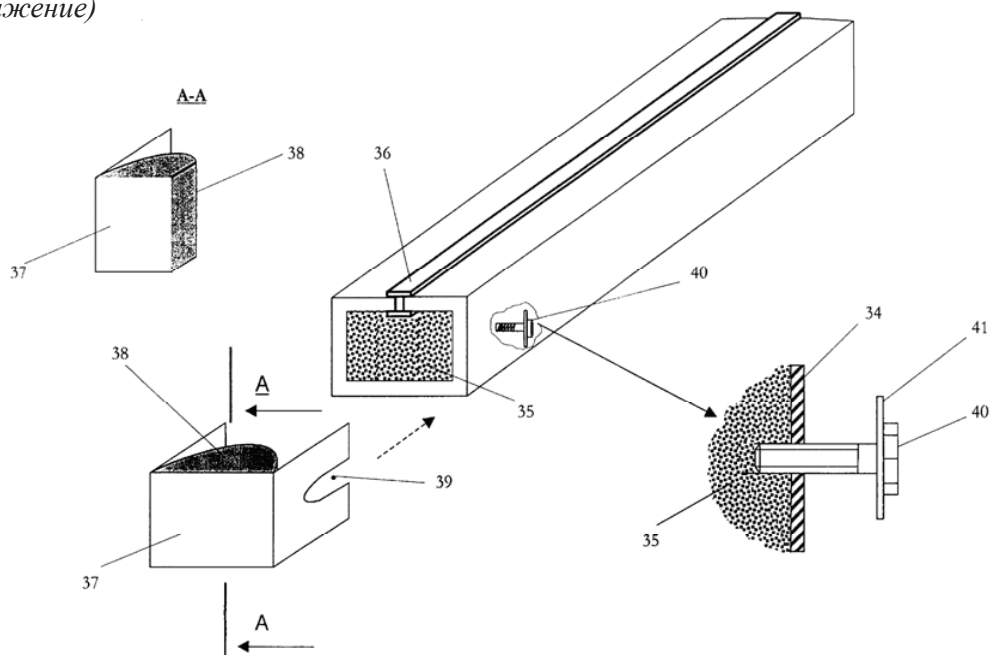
Схема фрагментов конструкции низкошумного акустического моторного стенда:
